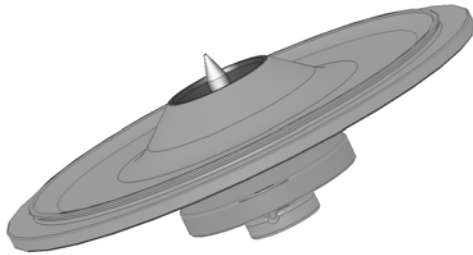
AutoLock™-Deckel für einen aerosoldichten Rotor
